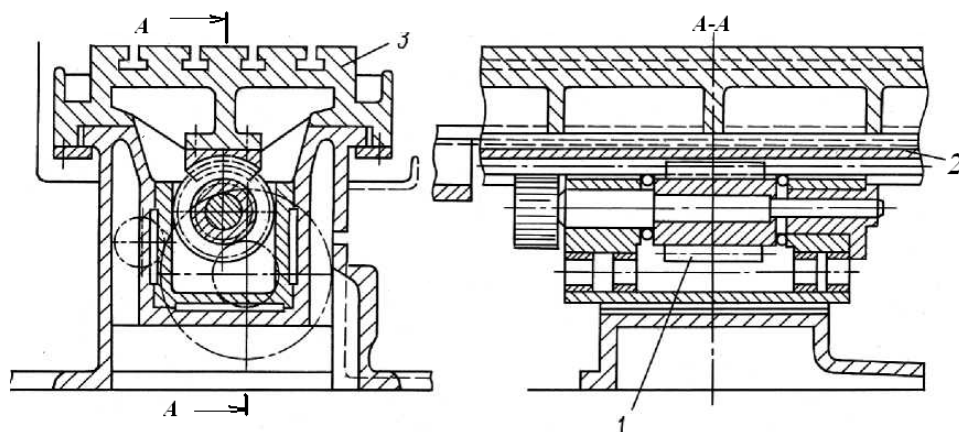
Червячно-реечный привод стола продольно-фрезерного станка
